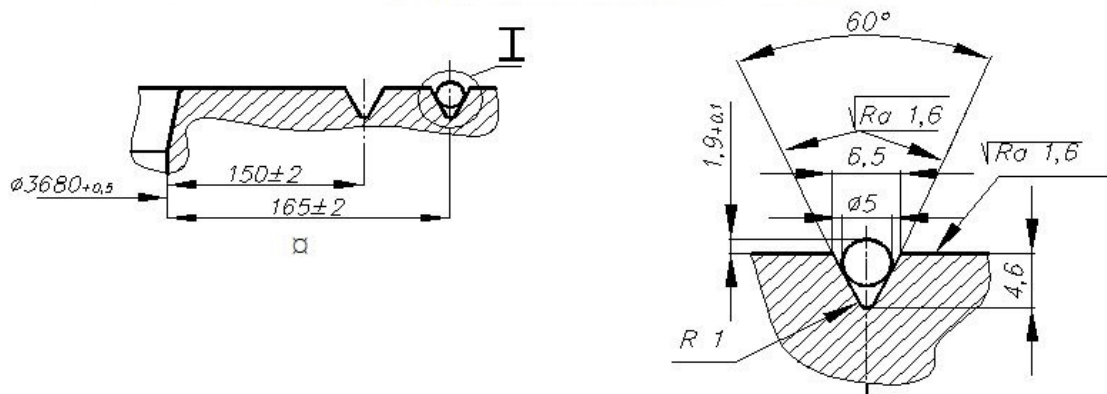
Ущільнююча поверхня головного роз'єму корпусу реактора
